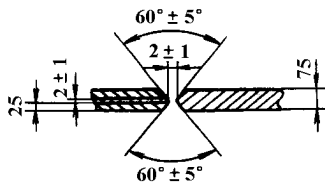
拼接焊缝坡口形式与尺寸
